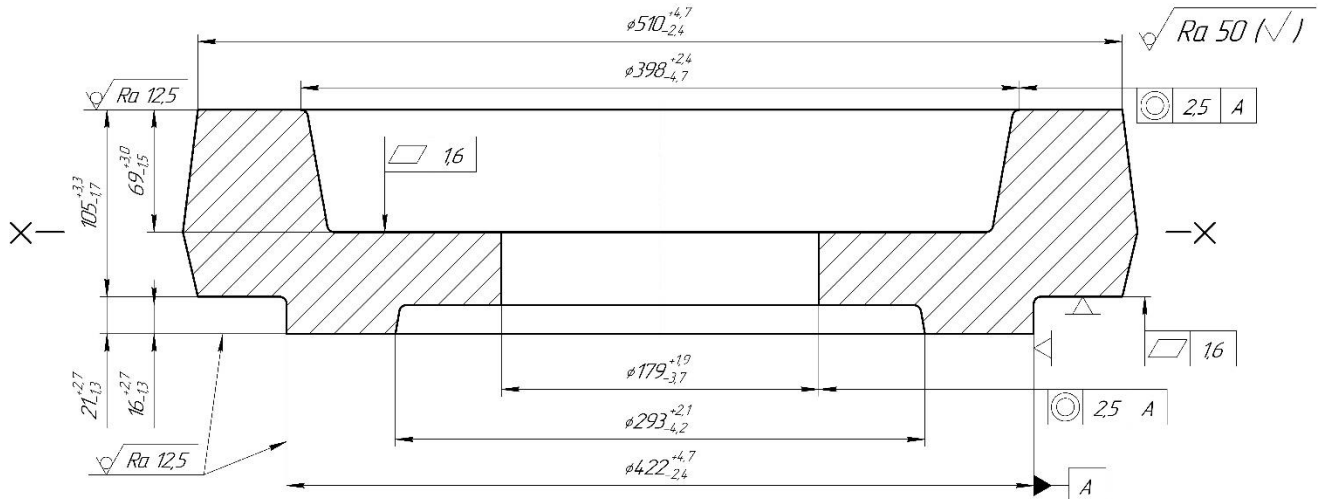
Штамповка, яка виготовлена на гідравлічному пресі
